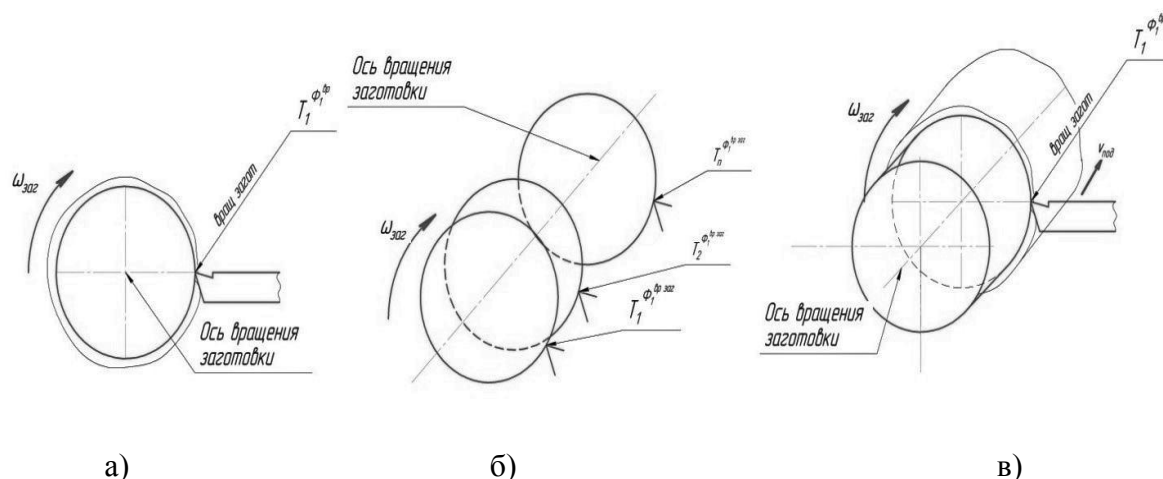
Структурная схема точечного взаимодействия инструмента с обрабатываемой поверхностью заготовки при ее вращательном движении:
